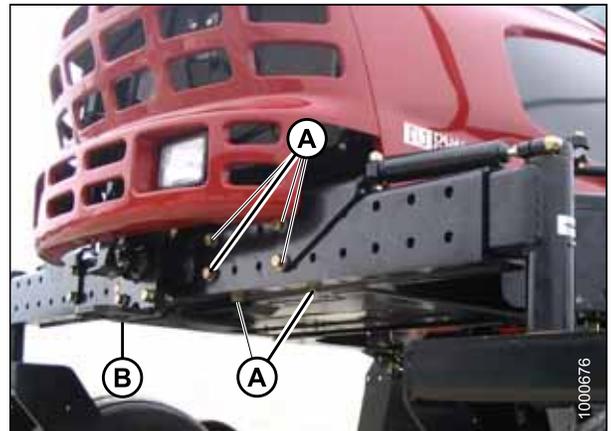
Удлинитель самоустанавливающихся колес
